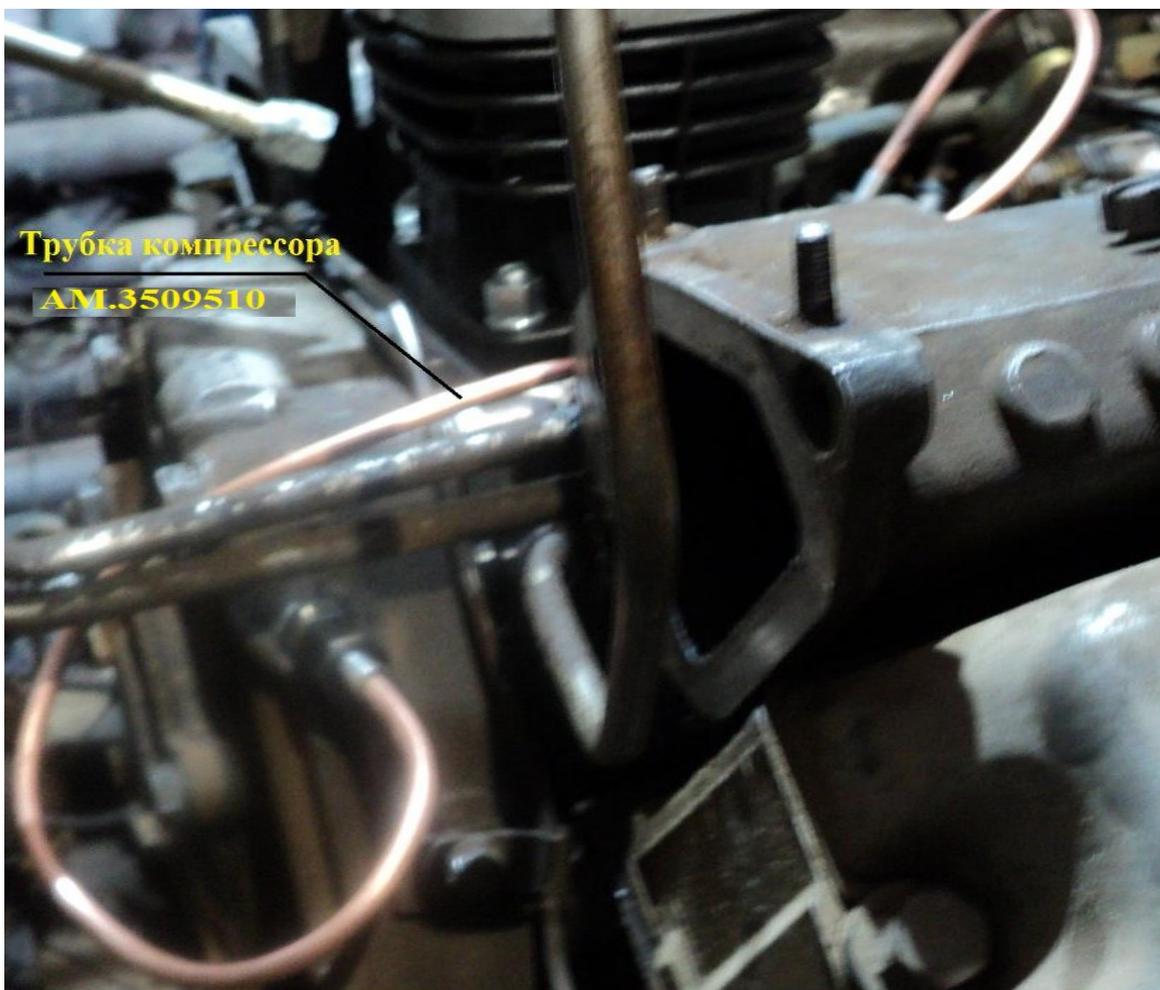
Установка Трубки компрессора 5642207-3509262 для подвода масла (поперечный воздушный коллектор снят).
